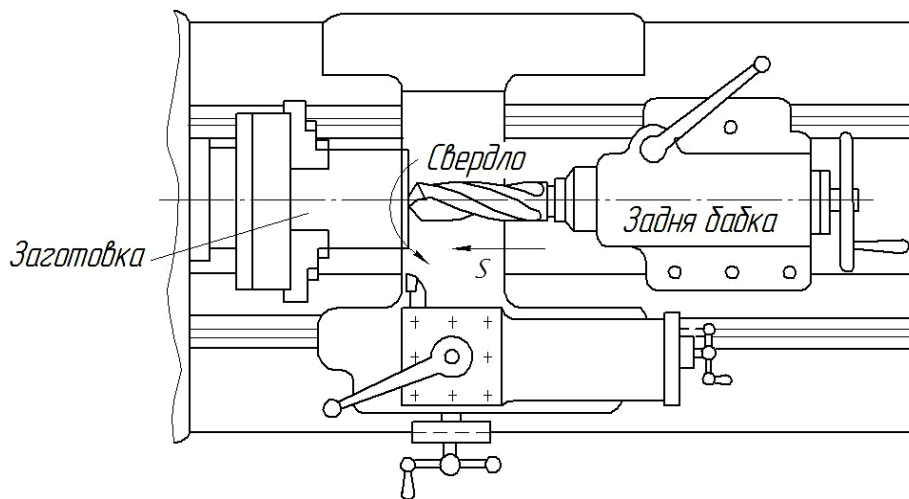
Свердління на токарному верстаті зі встановленням свердла у пінолі задньої бабки верстата
